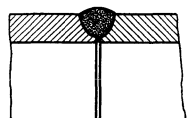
Tulpenförmige Ausbildung der Schweißnaht.
